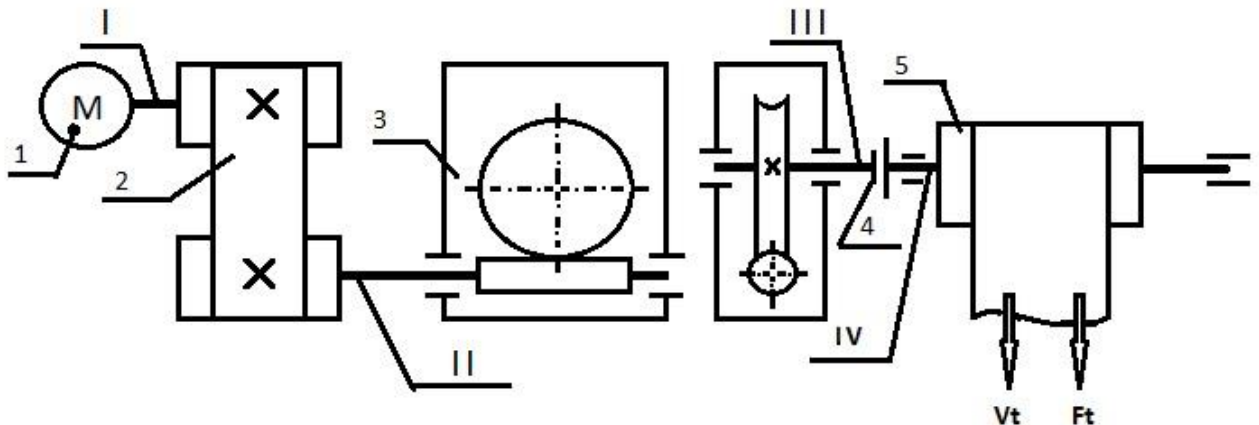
Кинематическая схема привода ленточного конвейера
